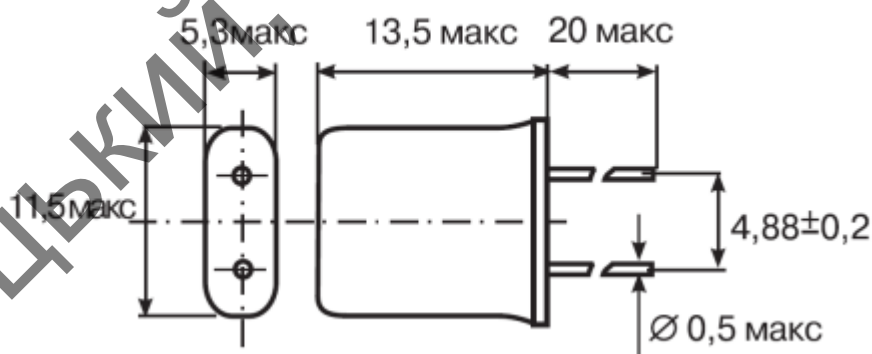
Кварцовий резонатор у корпусі *НС-49/У
